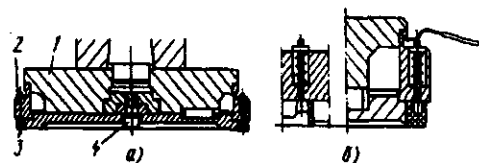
Торцовая фреза с креплением твердосплавных пластин подпружиненным плунжером: а – фреза; б – узел крепления
